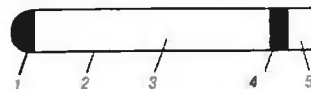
Зварювальний олівець: 1 — запалювальна головка; 2 — гілка; 3 — екзотермічна суміш; 4 — штик; 5 — порожнина для вставлення тримача
